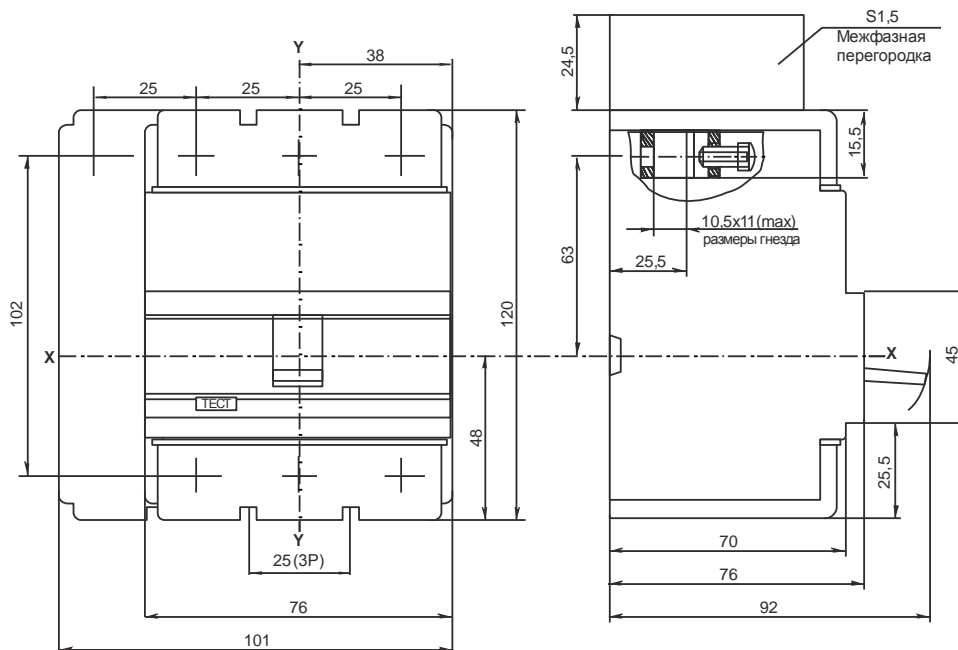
Габаритные и установочные размеры выключателя ВА88-32
